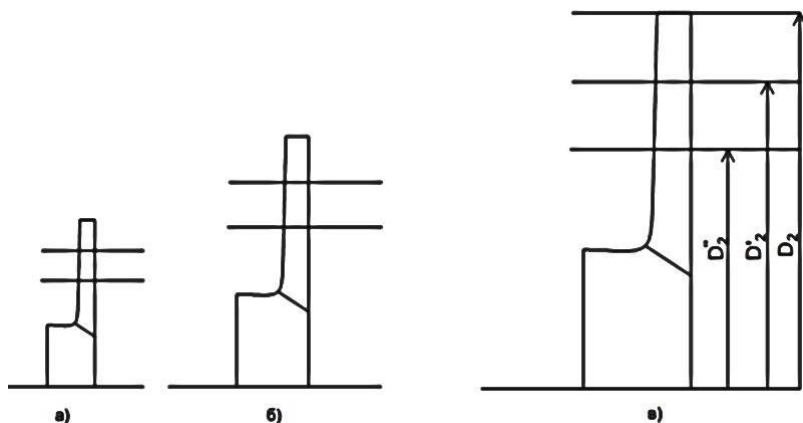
Робочі колеса з підрізанням по діаметру D_2
